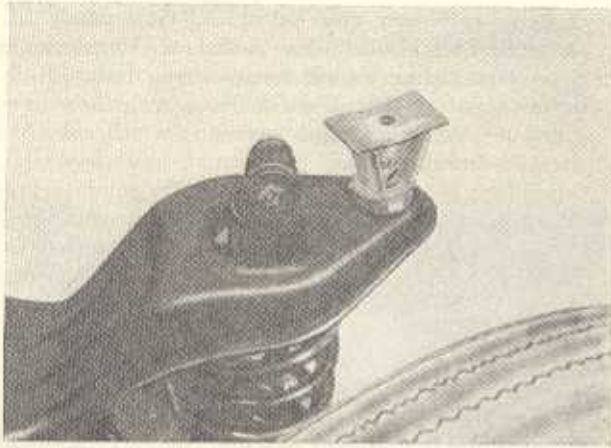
Hintere Karosseriebefestigung, Baumuster 312
